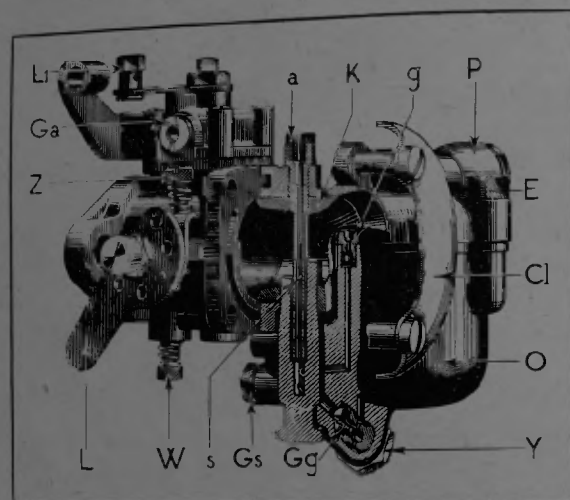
Vue en coupe partielle du carburateur 30 AHD.
